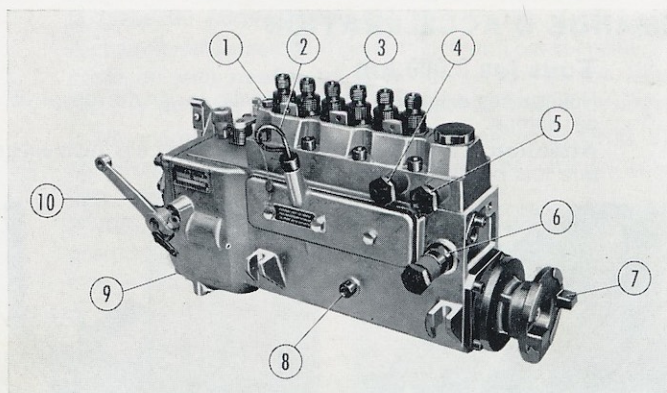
Vue d'ensemble de la pompe d'injection CBC - 6 cylindres.
